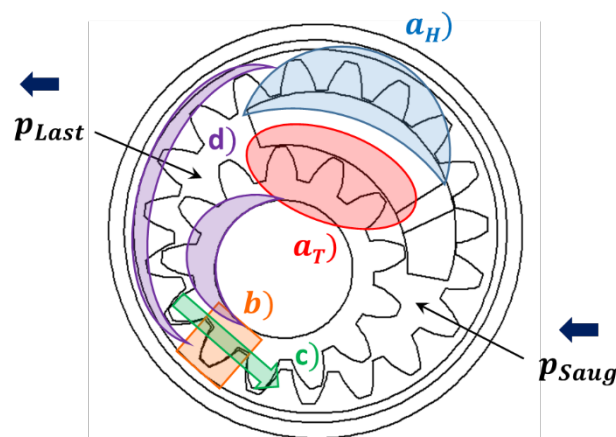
Leckagemechanismen einer Innenzahnradpumpe
